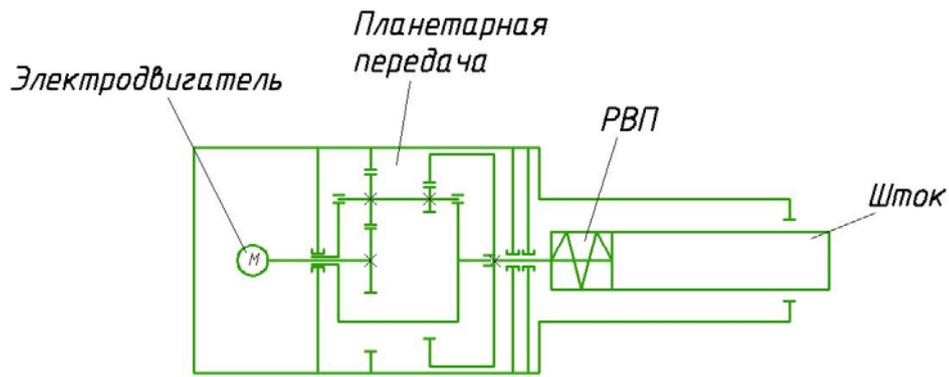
Кинематическая схема высокоточного линейного привода на основе РВП
